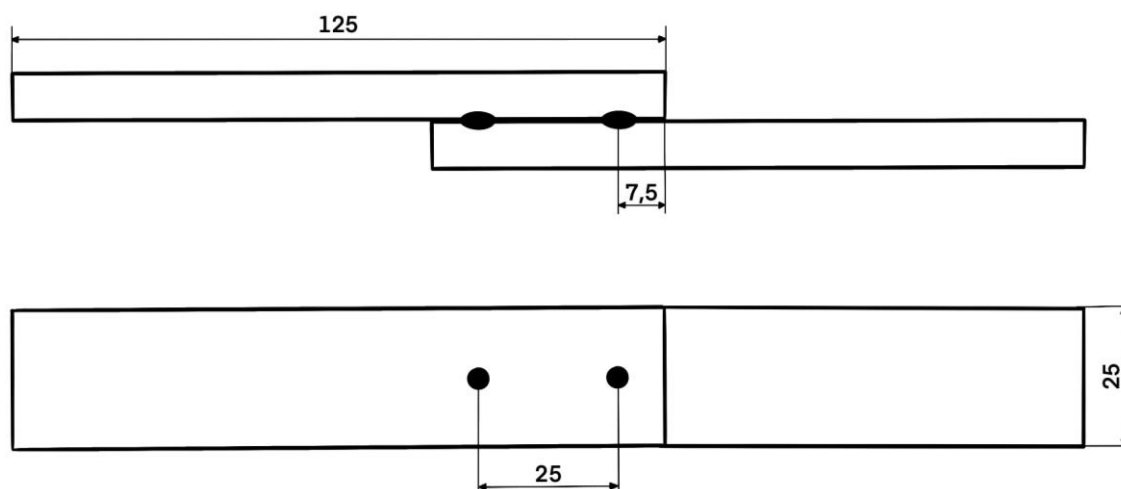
Representação esquemática da realização da soldadura das chapas com dois pontos de soldadura
